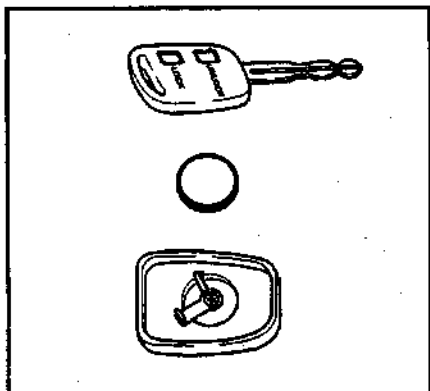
Установка батареи в корпус передатчика, расположенный в головке ключа
